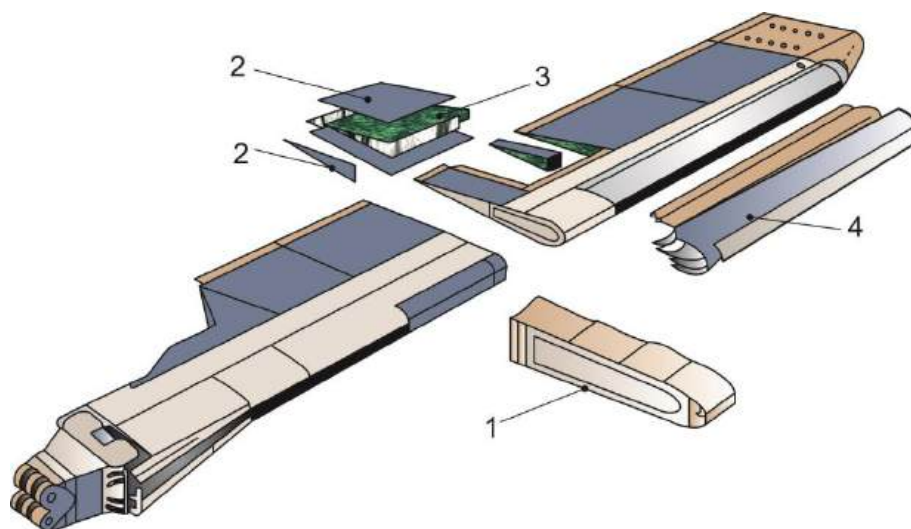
Схема розташування ПКМ у лопаті вертольота:
